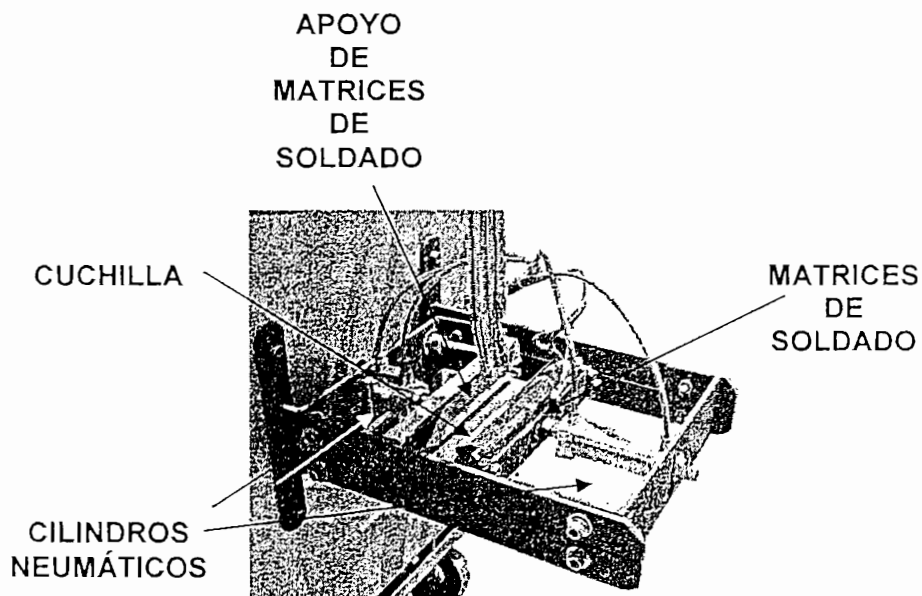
Conjunto de soldadura horizontal y corte de la funda
